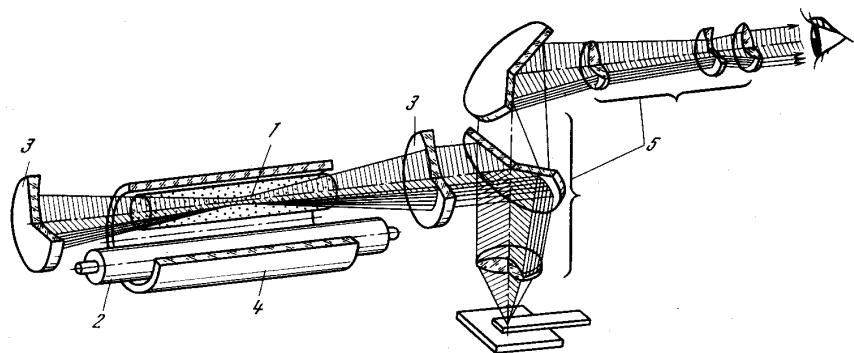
Схема лазерной сварки: 1 – стержень активной среды; 2 - лампа накачки; 3 – зеркала резонатора; 4 – зеркальный цилиндр осветителя; 5 – система фокусировки излучения на свариваемые детали и наблюдения за процессом сварки.
